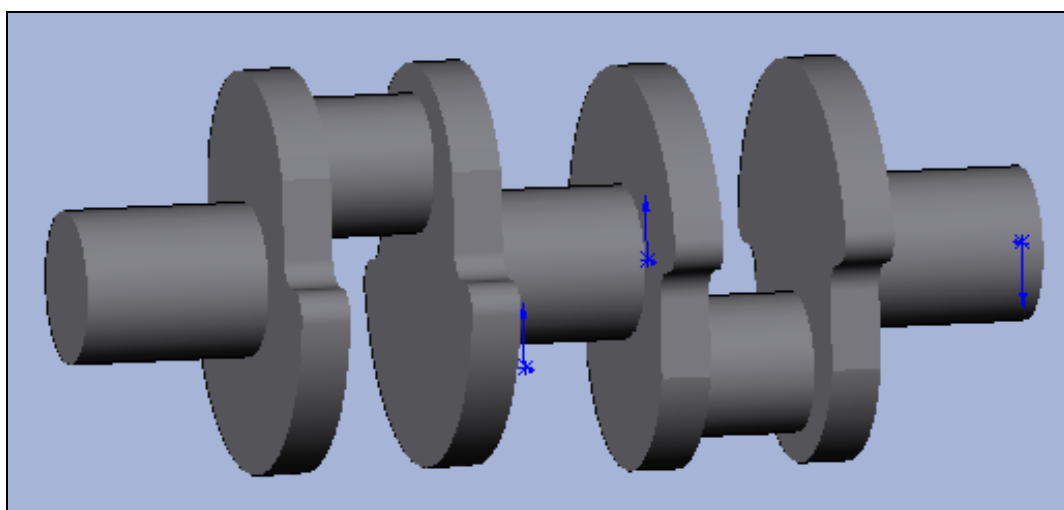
Коленчатый вал двухцилиндрового двигателя
